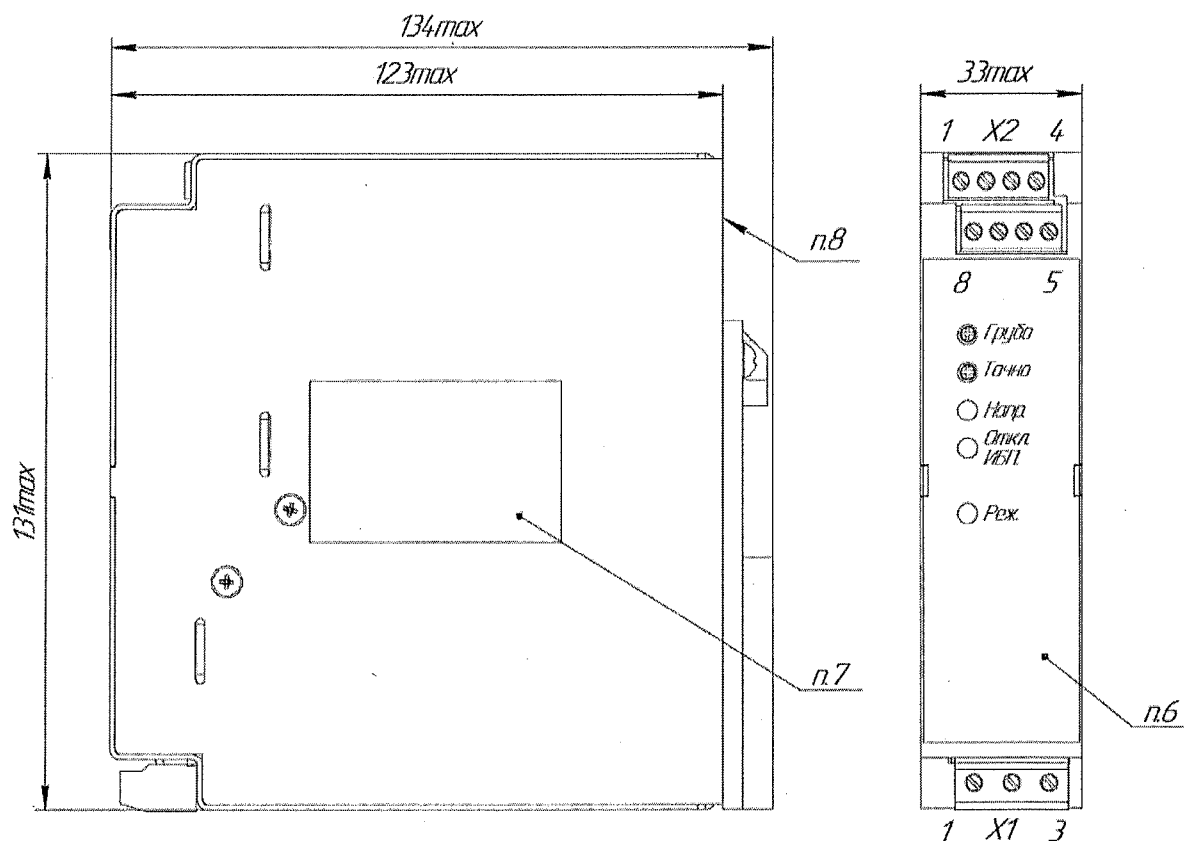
Габаритные размеры модуля КАН-Д75
